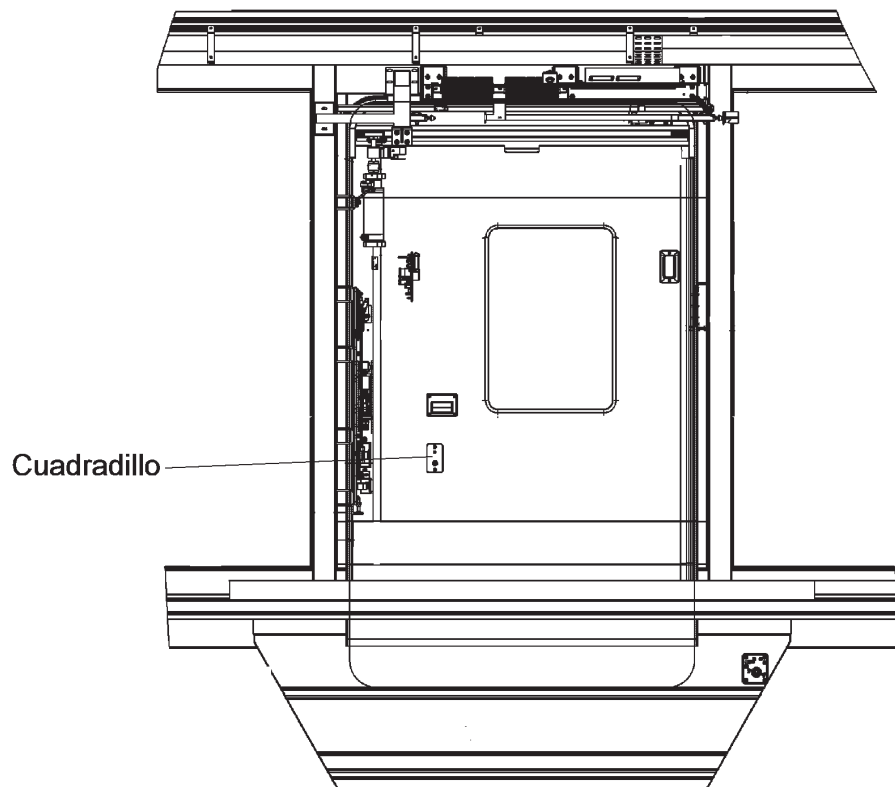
Condena de una puerta de acceso rampa - estribo
